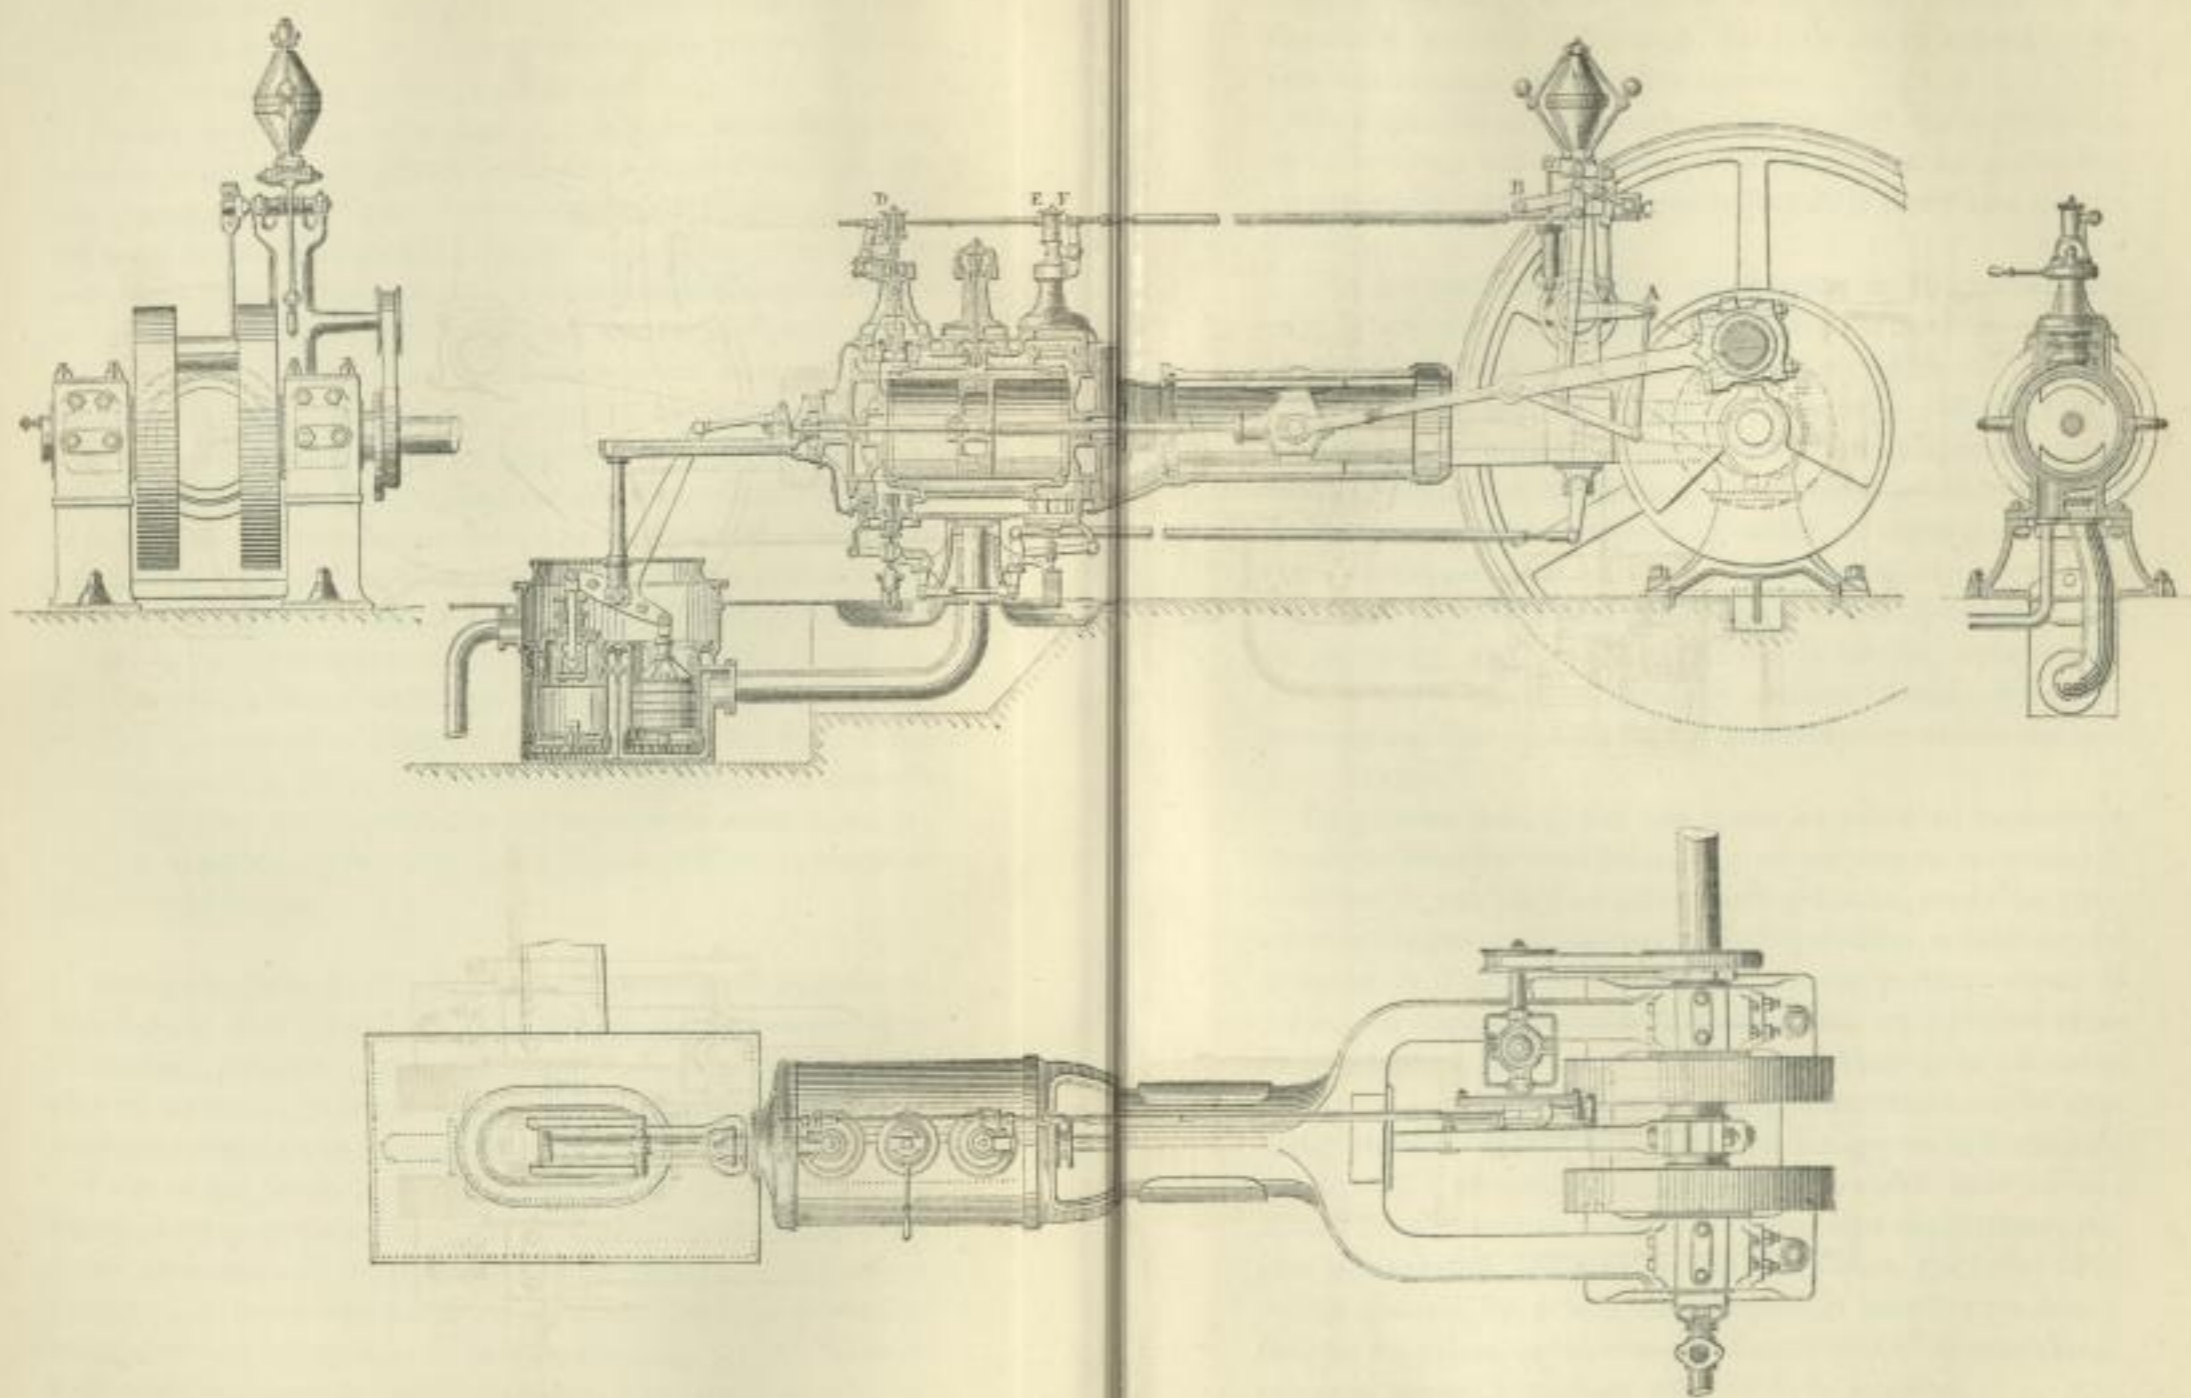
Machine à vapeur de la Société suisse de Winterthur.
